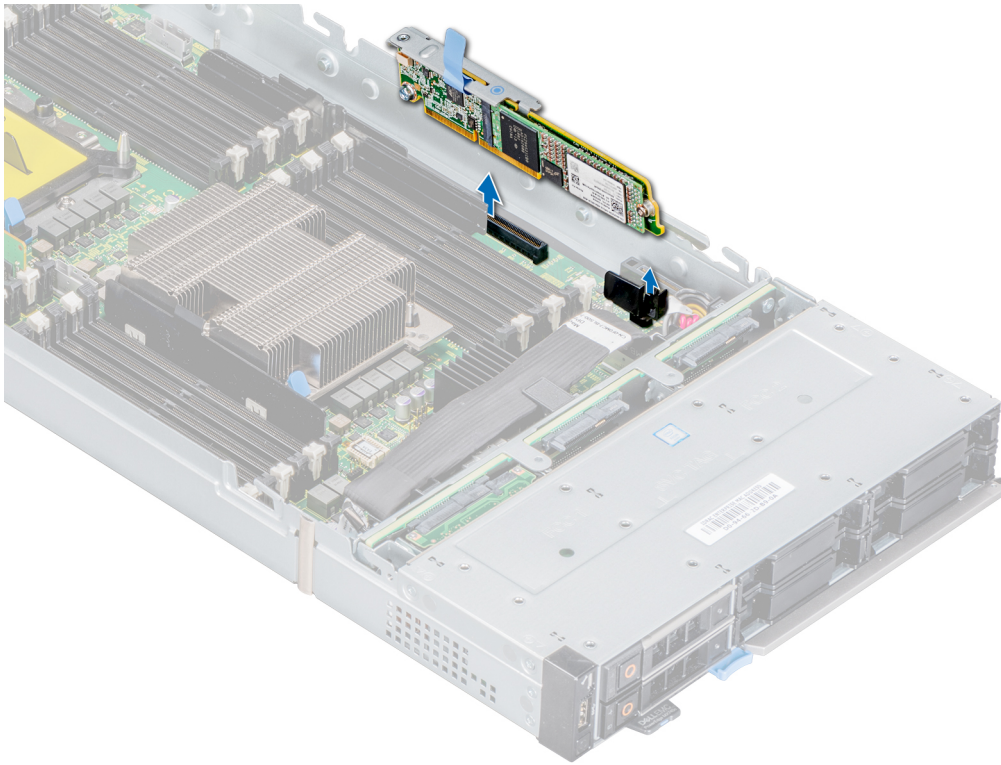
Entfernen des M.2-BOSS-Moduls
